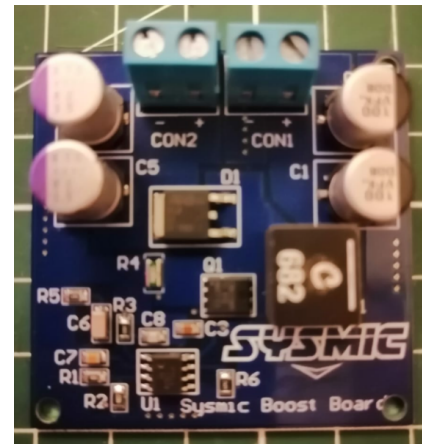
Fabricante Chino de tarjetas de circuito, PCBWay.
